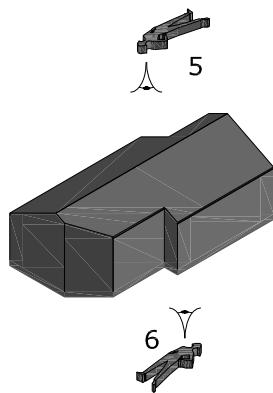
Positions de l'observateur pour des projections sur des plans verticaux
